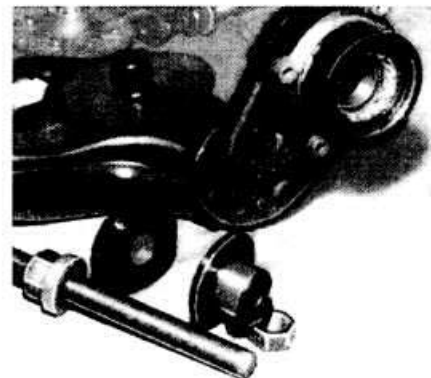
Запрессовка подшипника ступицы с помощью винтового пресса
